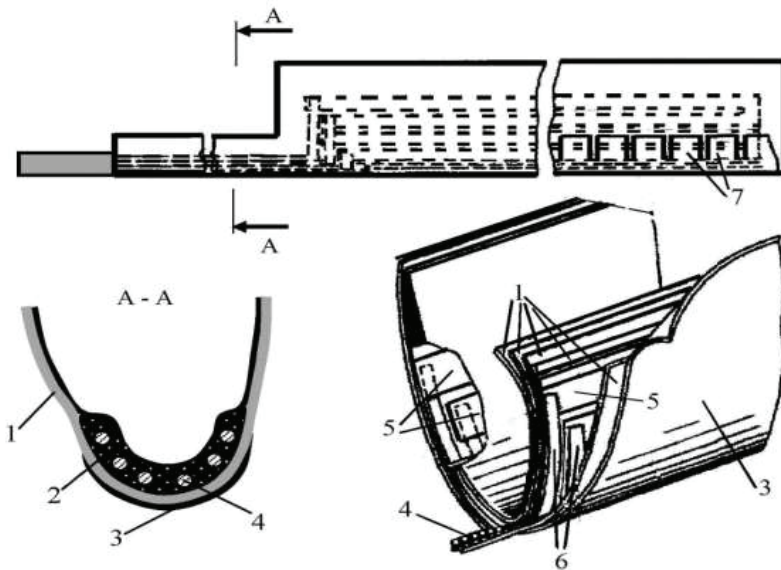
Нагревательные накладки лопасти несущего винта вертолета Ми-171, где 1 – слой стеклоткани; 2 – клеевой наполнитель; 3 – абразивный слой резины; 4 – силовые электропровода; 5 – нагревательные элементы; 6 – соединительные шинки; 7 - оковка
